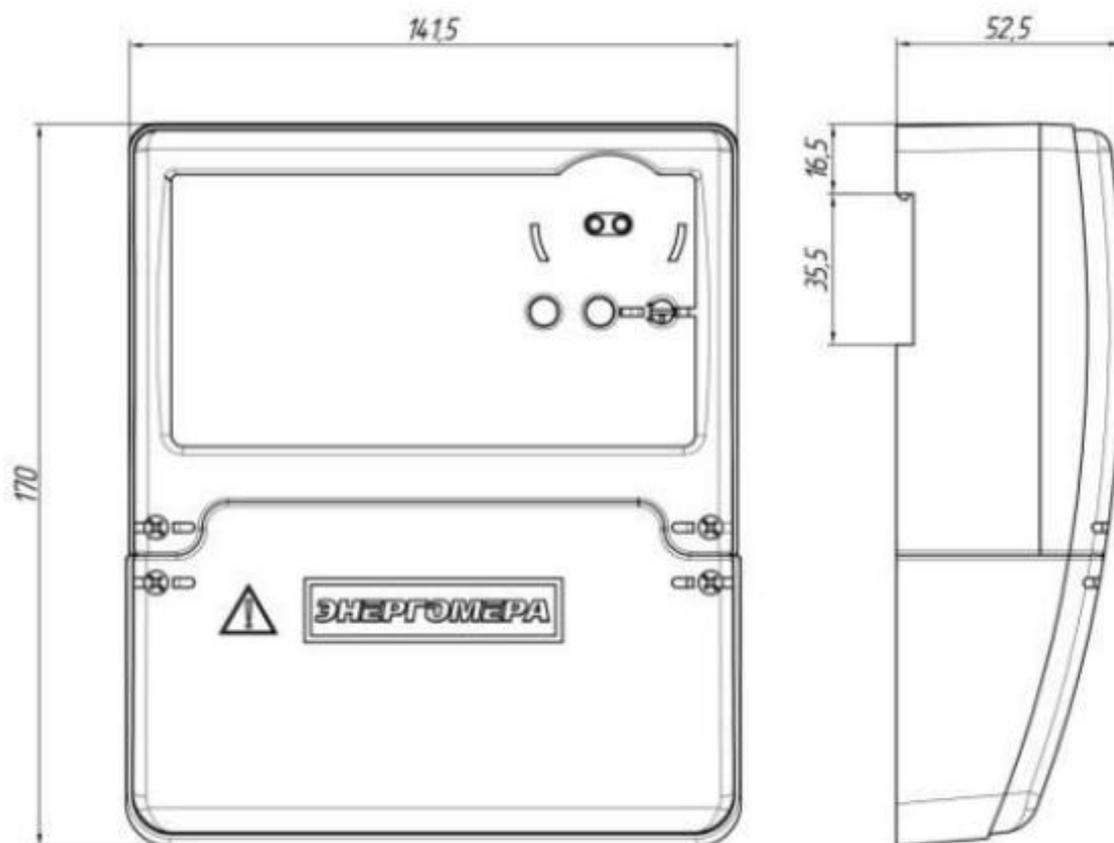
Общий вид счетчика в корпусе S35
